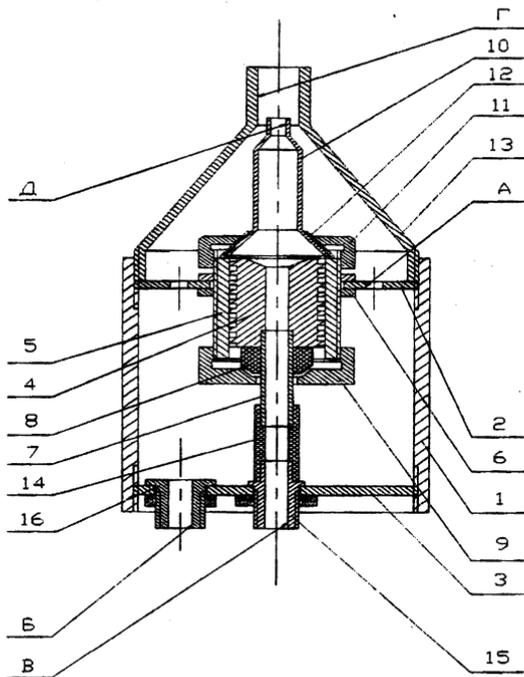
Устройство для изготовления сферических носителей катализаторов
